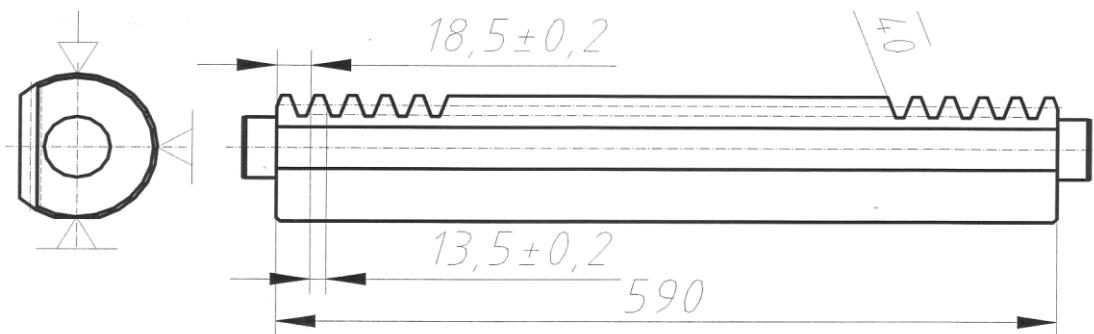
Ескіз обробки деталі операція №050
